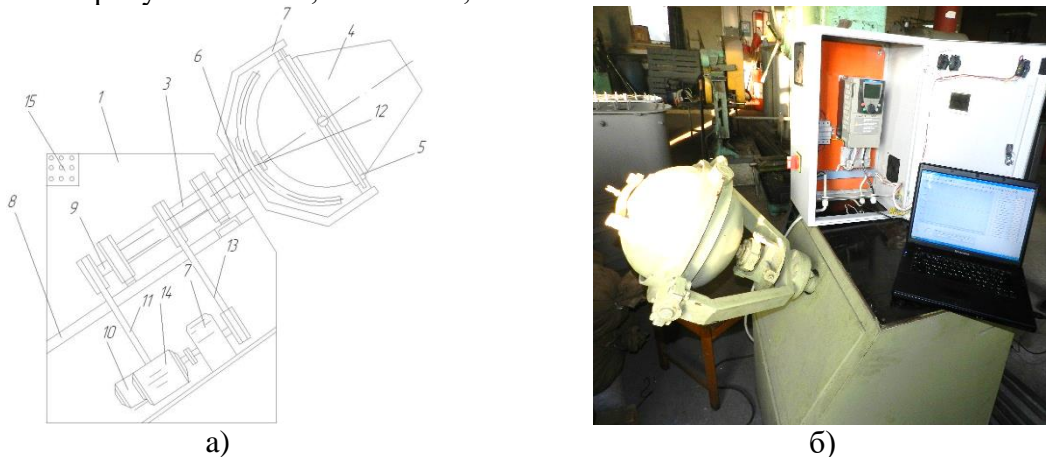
Конструктивна схема вібраційно-відцентрової установки а)
